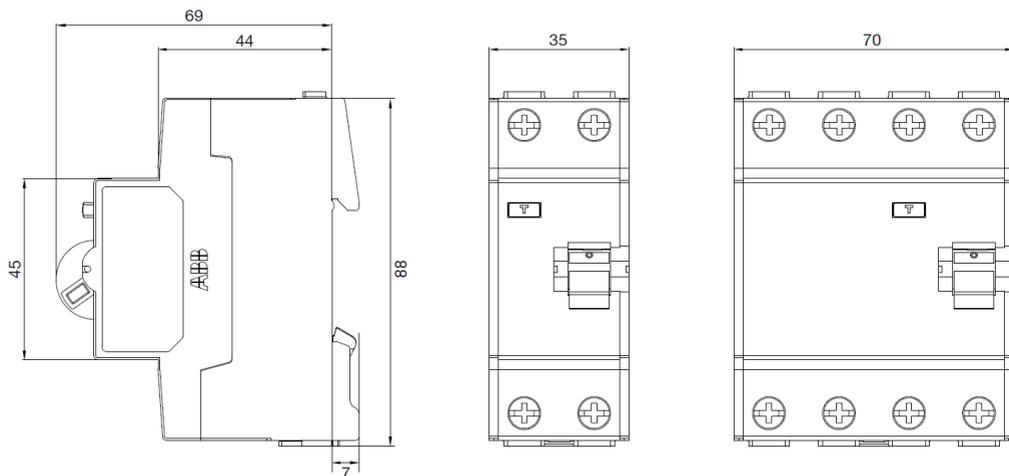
Габаритные, установочные и присоединительные размеры ВДТ серии VMF, мм.
